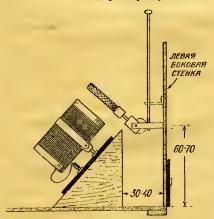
Крепление катушки L_1 и устройство подвижного станочка для катушки обратной связи.
